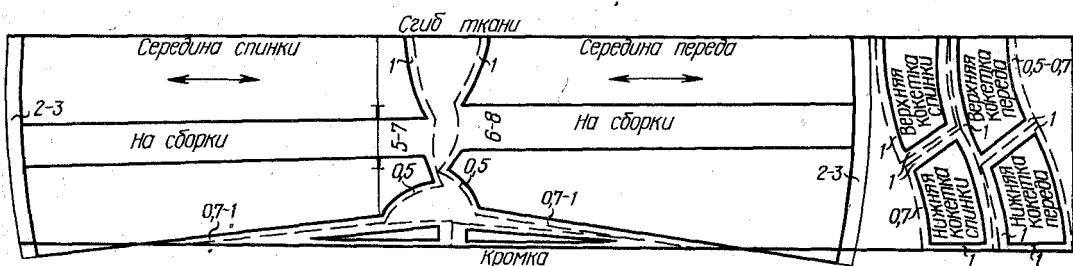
Раскладка выкроек на ткани и раскрой сорочки на круглой кокетке
